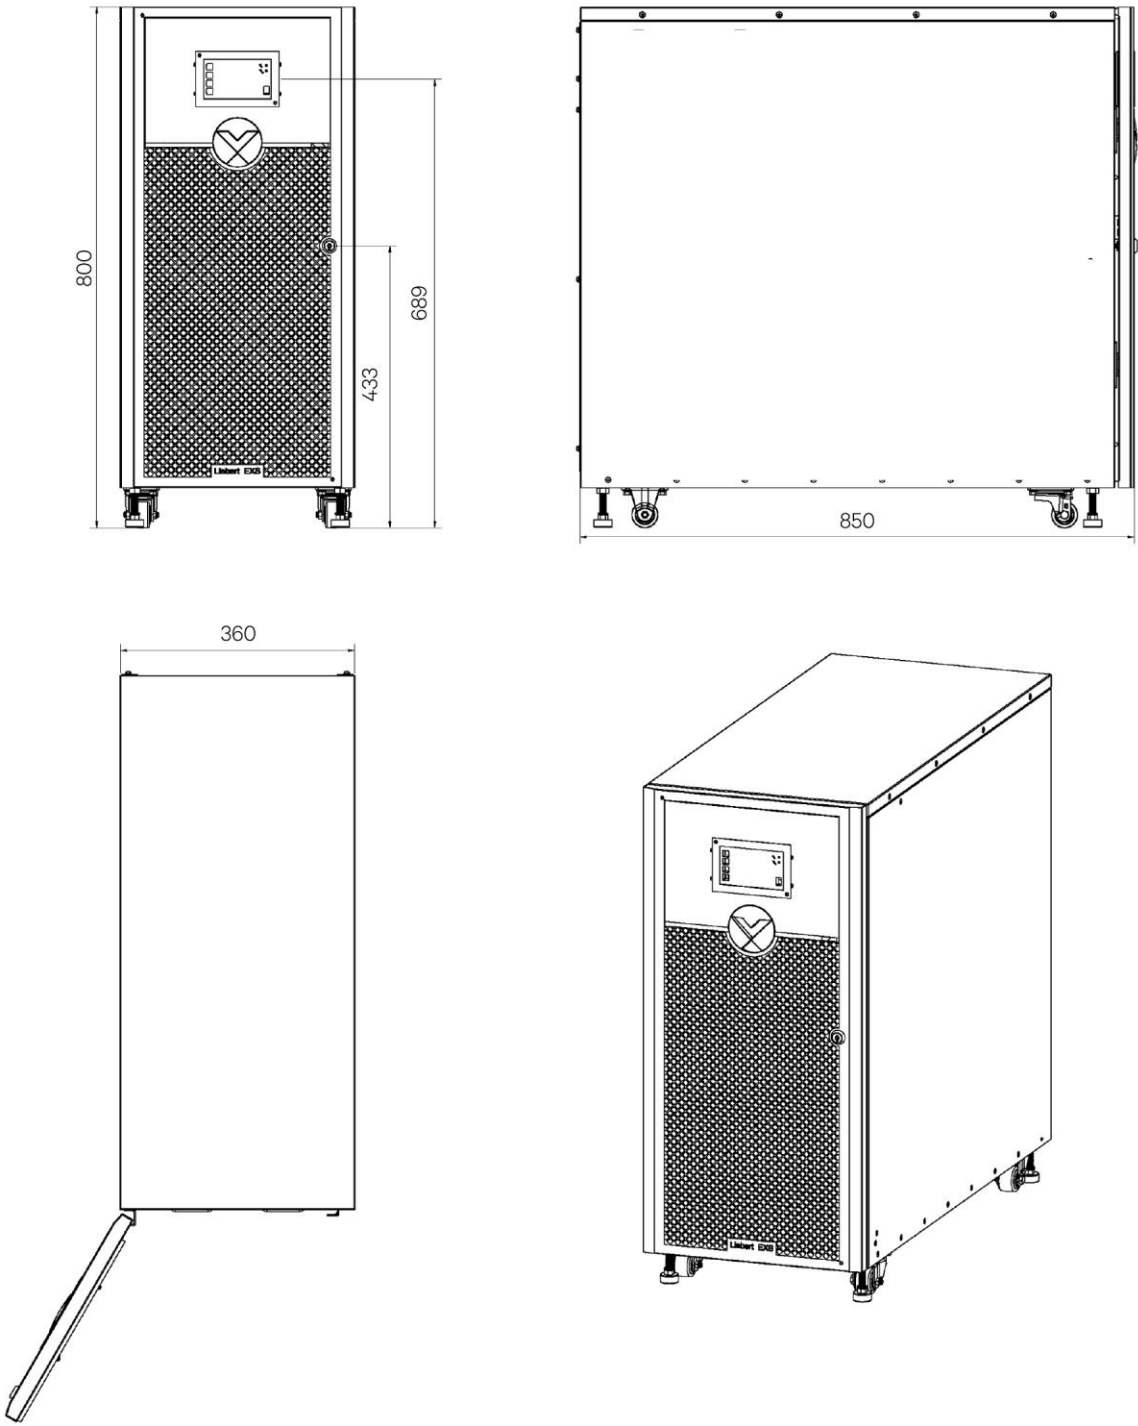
60k/80k UPS 机柜安装尺寸示意图 (单位: mm)
